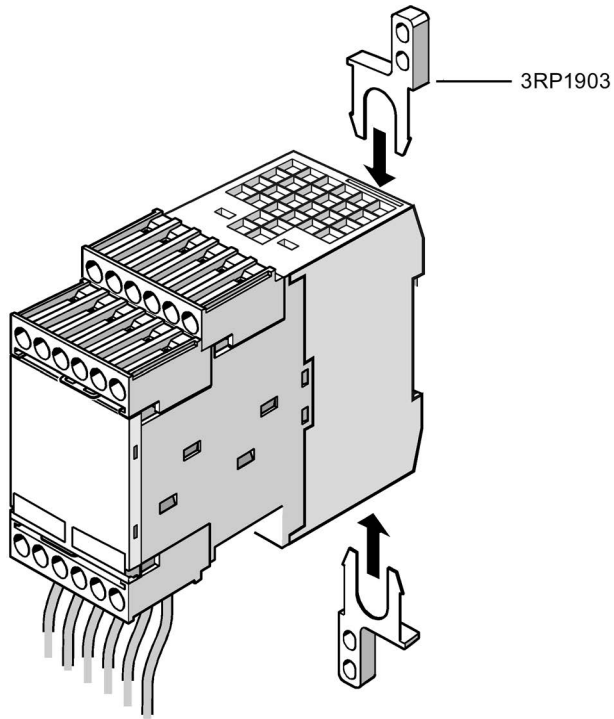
Befestigung des DM-F mit Hilfe von Einstecklaschen für Schraubbefestigung
